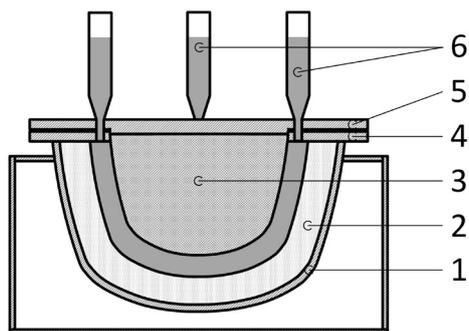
Детали одной из возможных конфигураций формовочного комплекта для литья керамических заготовок из водных шликеров: перфорированный металлический каркас (1), влагопоглощающая форма (2), непористый сердечник (3), опорный металлический фланец каркаса (4), металлический фланец сердечника (5), подпиточные емкости для шликера (6)
